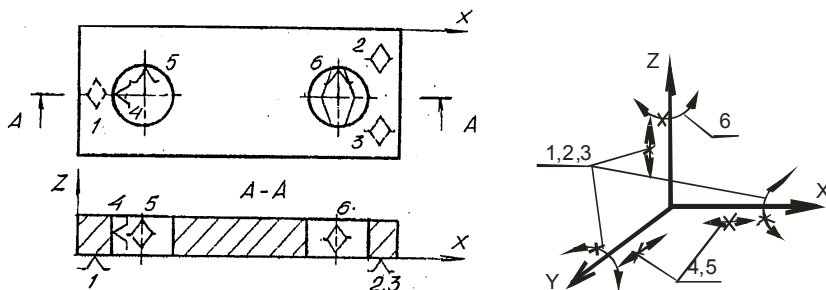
Теоретическая схема базирования заготовки по плоской поверхности и двум отверстиям
